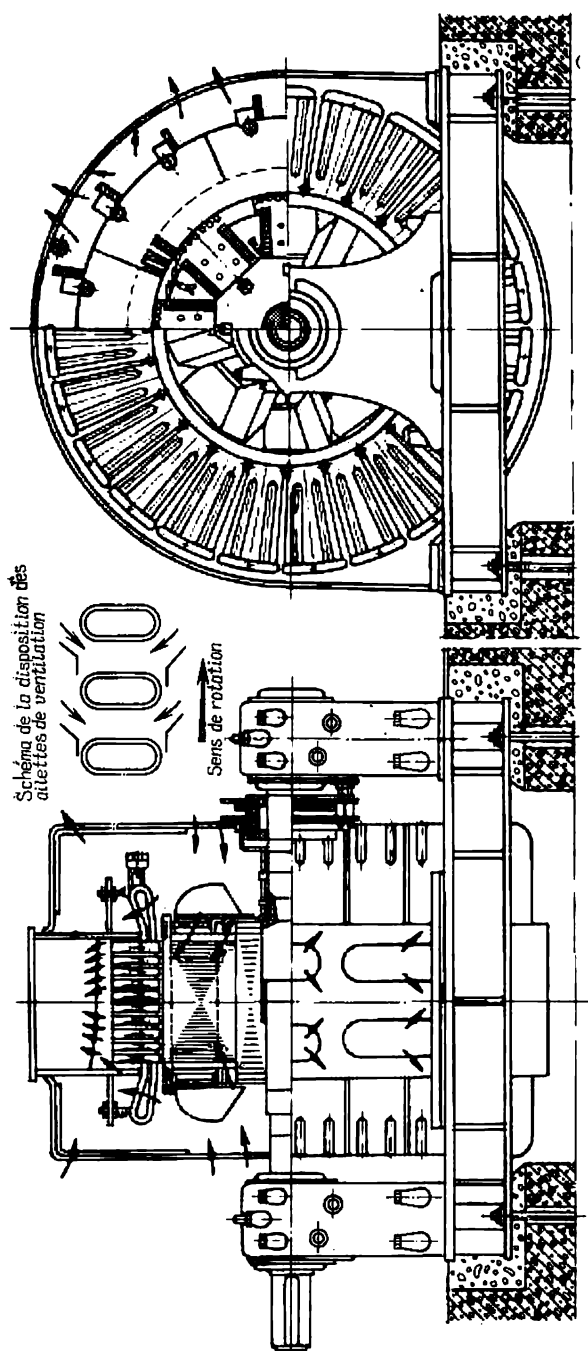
Machine synchrone de la série CГН (ou CДН) en version ouverte.
